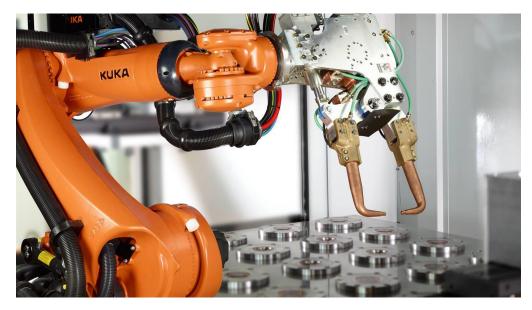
Роботизированный манипулятор для контроля размеров, формы и других параметров заготовок.
